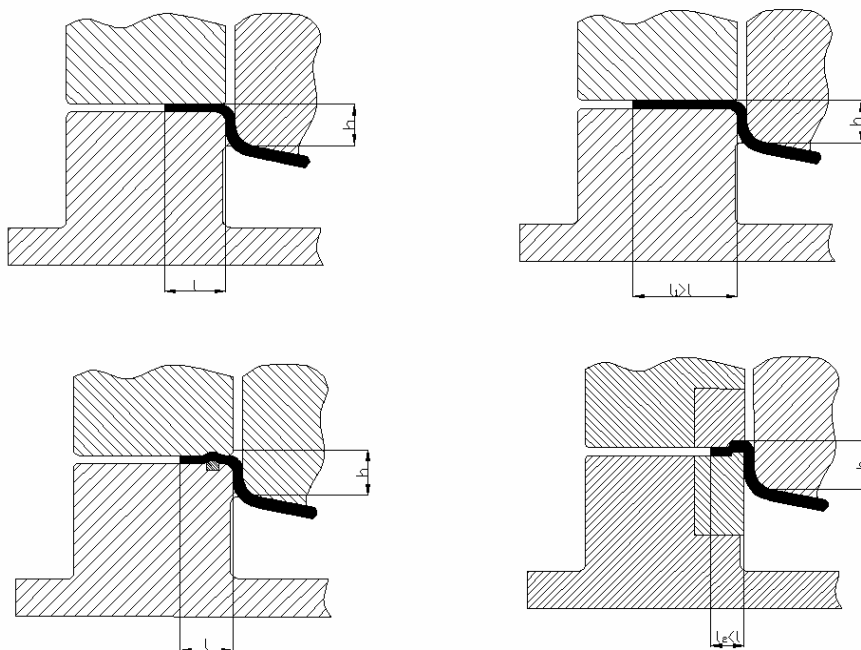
Различные способы увеличения интенсивности торможения фланца заготовки под прижимом.
